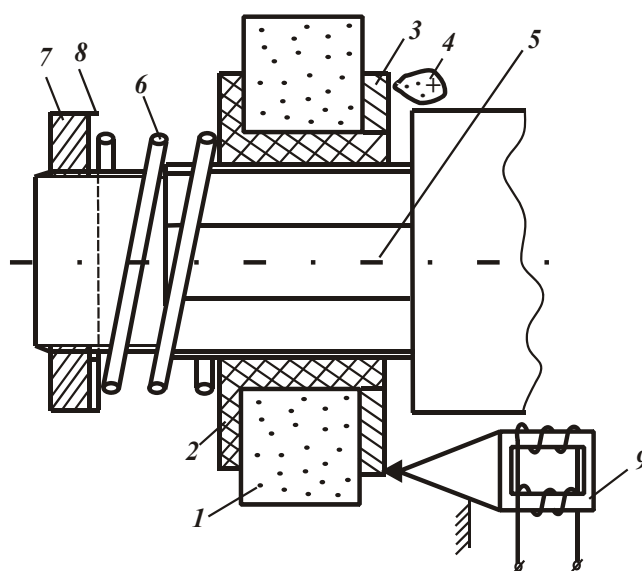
Устройство с осевым перемещением шлифовального круга: 1 – круг; 2 – шлицевая втулка; 3 – прижимная шайба; 4 – эксцентрик (показан повернутым на 90°); 5 – шлицевый вал с резьбой; 6 – пружина; 7 – гайка; 8 – шайба; 9 – магнестрикционная колебательная система.
